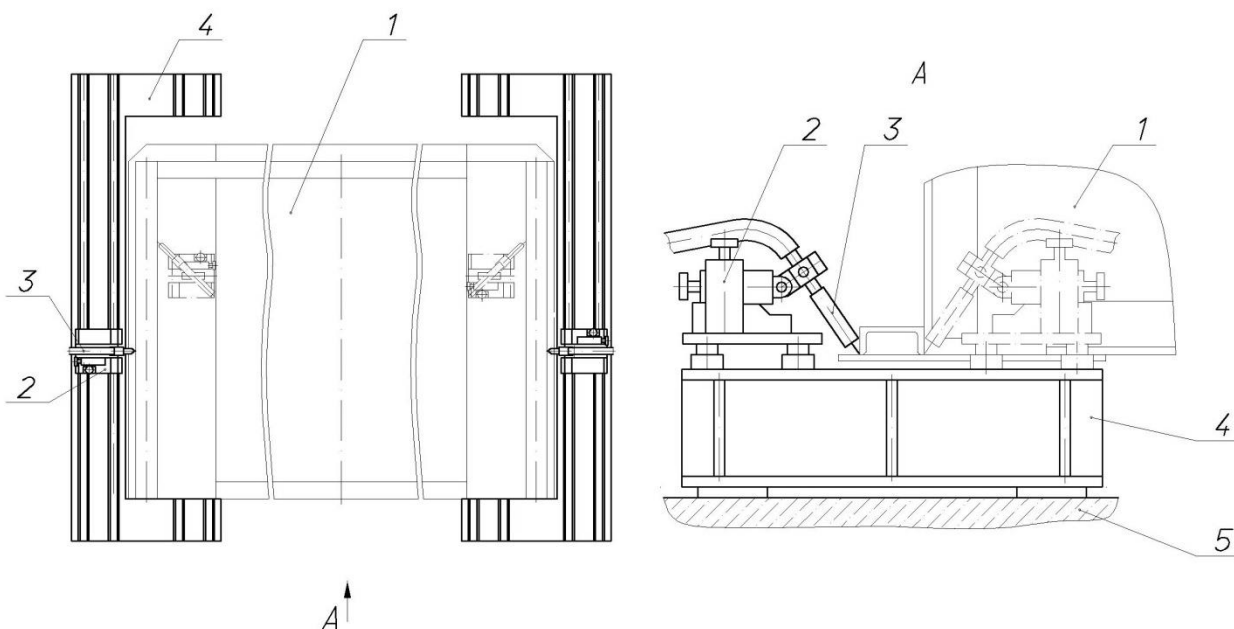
Схема автоматической сварки основных вертикальных швов кузова полувагона: 1 – кузов полувагона повернутый на 90° (вертикальные швы приведены в горизонтальное положение); 2 – сварочный трактор MagTracF-61; 3 – сварочная горелка трактора; 4 - съёмная балка для установки сварочных тракторов и их заезда во внутрь кузова при сварке; 5 – фундамент станда
